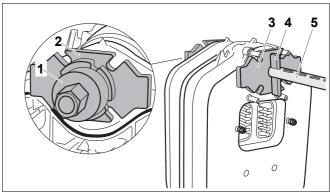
Strettoio di montaggio montato sul mozzo superiore
